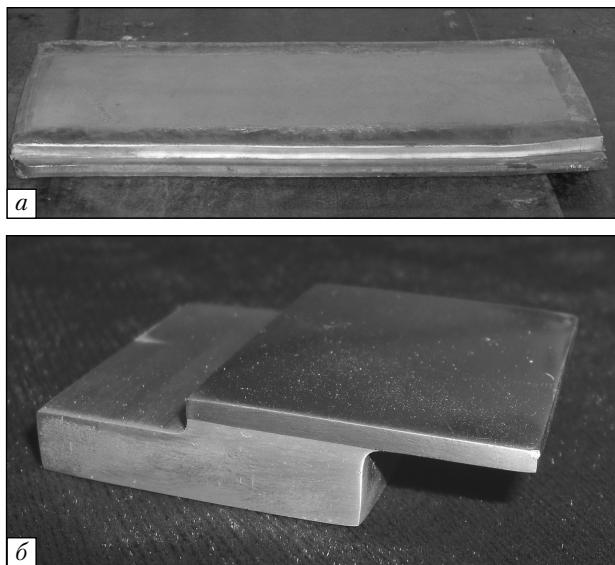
Биметаллическая заготовка (сталь-алюминиево-оловянный сплав) для изготовления подшипников скольжения (а) и подшипники скольжения (б)
